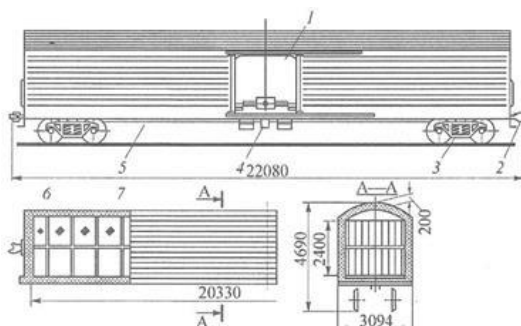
Вагон-термос: 1—дверь; 2—автосцепка; 3—тележка; 4—пневматический тормоз; 5—стояночный тормоз; 6—защитная стенка; 7—напольные решетки
